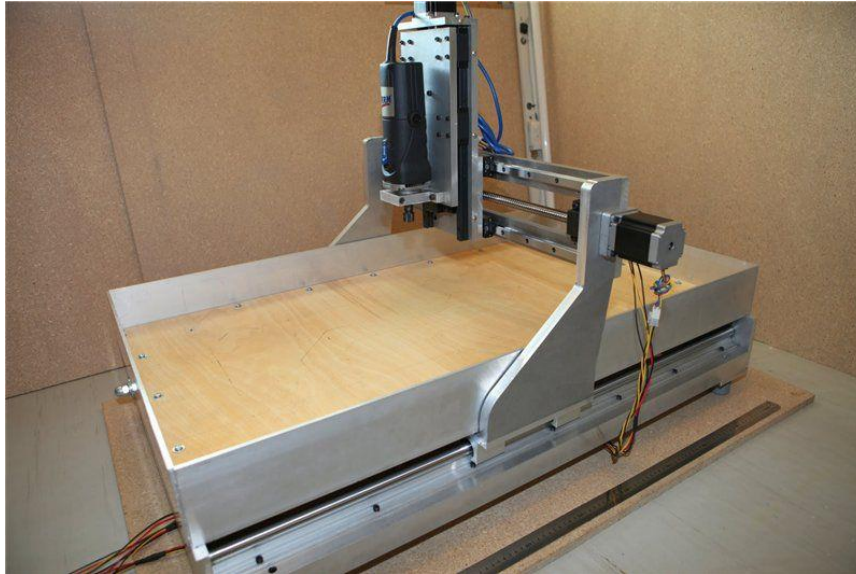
Типова конструкція та виконання непрофесійного фрезерного верстату з ЧПК
